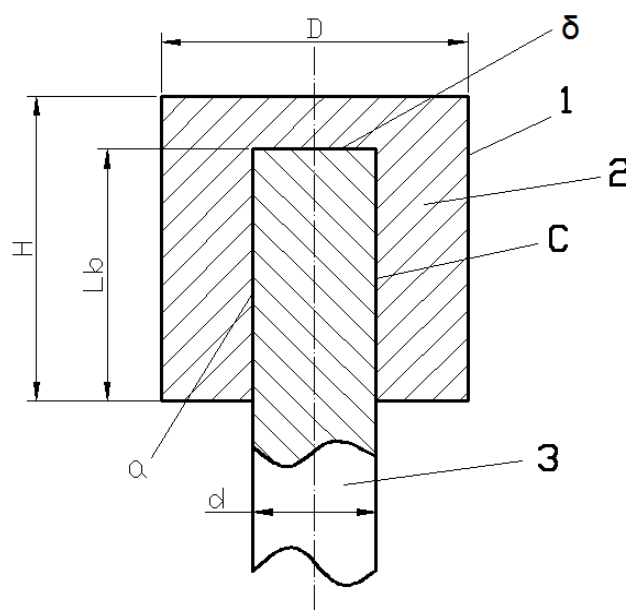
Сборная неразъемная заготовка (1), состоящая из элементарных заготовок: головной (2) и стержневой (3)
